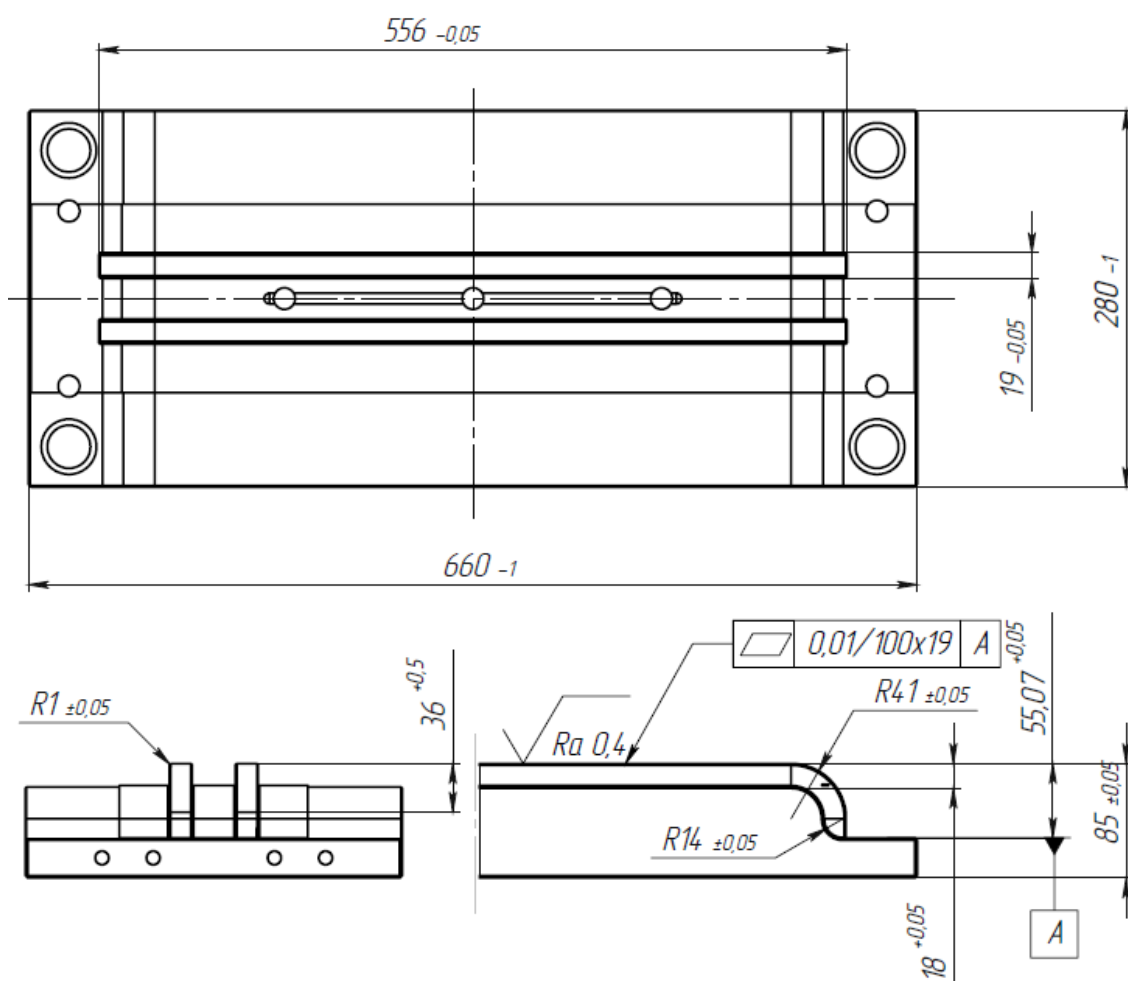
Эскиз формообразующего пуансона пресс-формы «Накладка»
